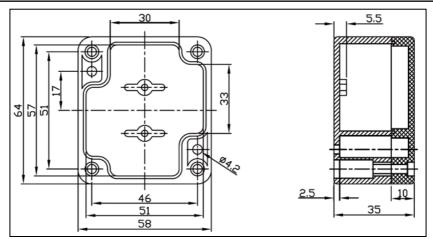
Разветвитель интерфейсный серии ИР. Габаритные размеры корпуса
